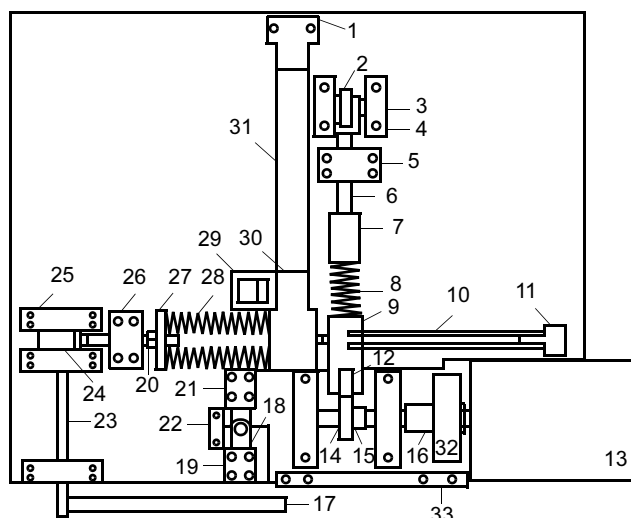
Схема производственной установки для СЛТ [10]: 1 — узел крепления фиксаторов; 2 — регулятор механизма передаточного рычага; 3 — основной вал; 4 — основные поддерживающие блоки; 5 — блок с ползуном возвратного перемещения; 6 — ползун с тензометром обратной пружины; 7 — локатор; 8 — возвратная пружина; 9 — колеблющийся фиксатор; 10 — параллельные балки; 11 — опора, поддерживающая колеблющийся фиксатор; 12 — кулачковый следящий элемент; 13 — муфта; 14 — вал кулачка; 15 — кулачок; 16 — плечо для приложения осевого усилия; 17 — шарнирный рычаг; 18 — шарнирно-рычажные узлы; 19, 21 — шарнирно-рычажные узлы; 20 — ползун и регулятор осевой пружины; 22 — ограничитель шарнирно-рычажного блока; 23 — вал кулачка, включающего осадку; 24 — устройство для передачи усилияковки; 25 — кулачковый блок; 26 — ползун осевой пружины; 27 — направляющий упор осевой пружины; 28 — осевая пружина; 29 — механизм освобождения фиксатора; 30 — неколеблющийся фиксатор; 31 — балки, параллельные фиксаторам; 32 — маховик; 33 — усиление жесткости плиты двигателя
